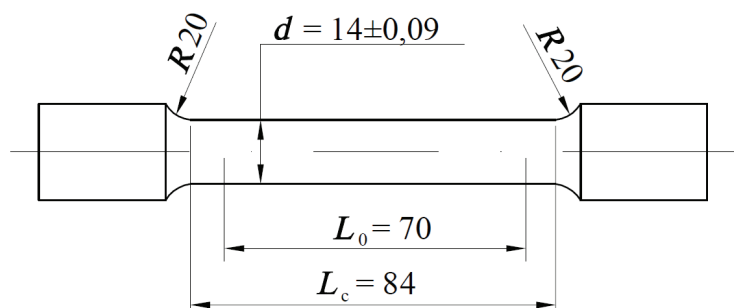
Образец для определения прочности отливок из высокопрочного чугуна: L_c – рабочая длина образца
